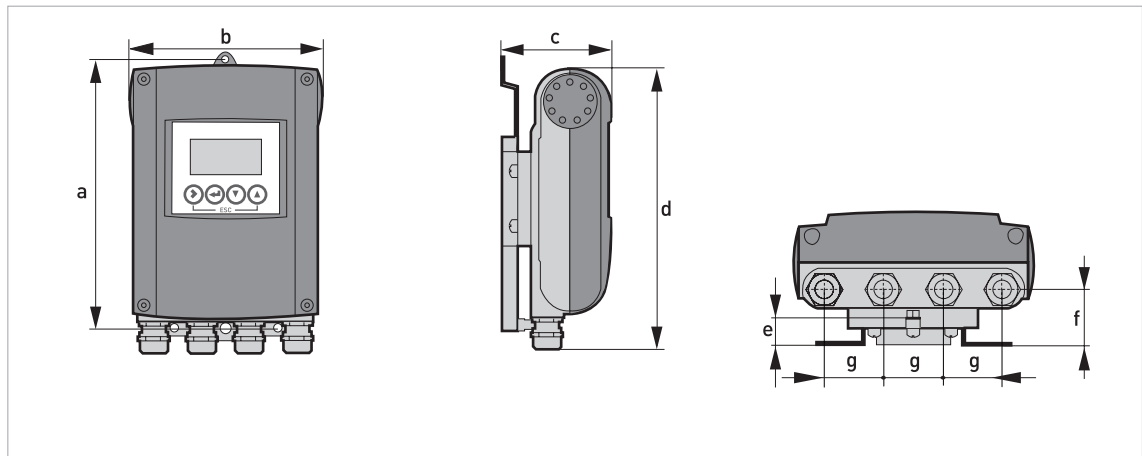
Abmessungen für Wand-Ausführung, Aluminiumgehäuse
